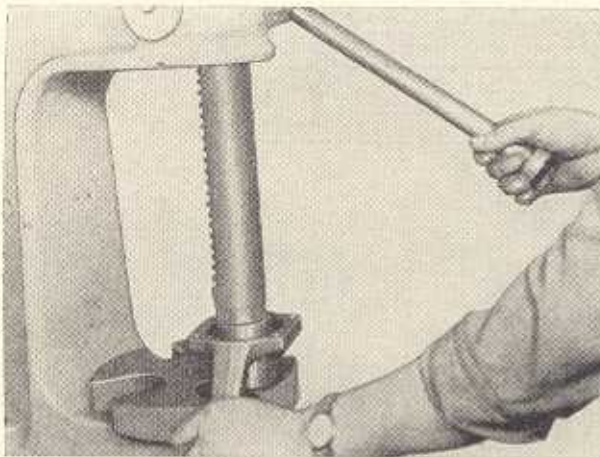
Einpressen des Wellendichtringes in das Schwenklager (W-210 747)
